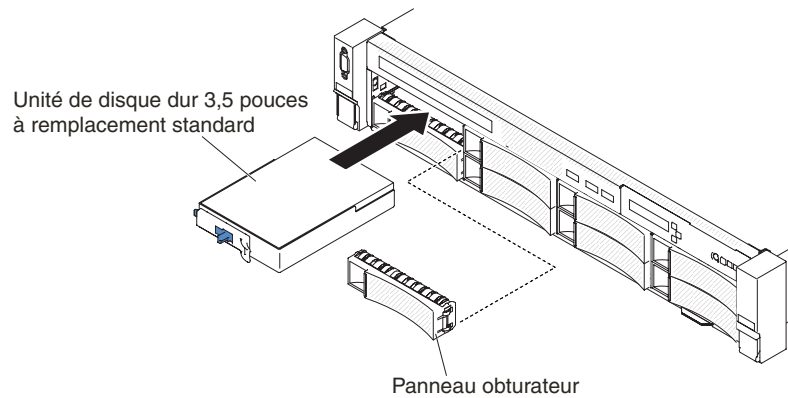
Installation d'une unité de disque dur à remplacement standard de 3,5 pouces
